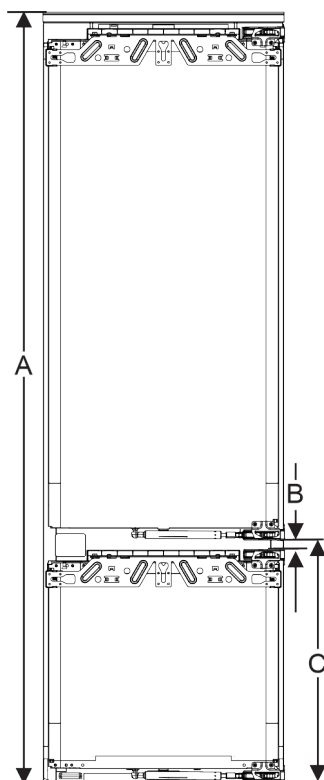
Posizione delle fughe parte frontale del mobile a due porte
